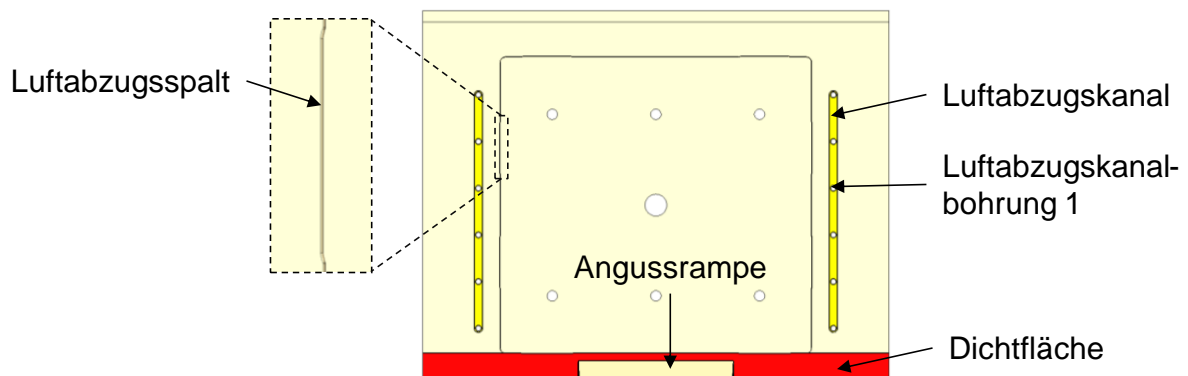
CAD-Darstellung eines Bottom-Werkzeugeinsatzes mit den wesentlichen Merkmalen für den Werkzeugbau.
